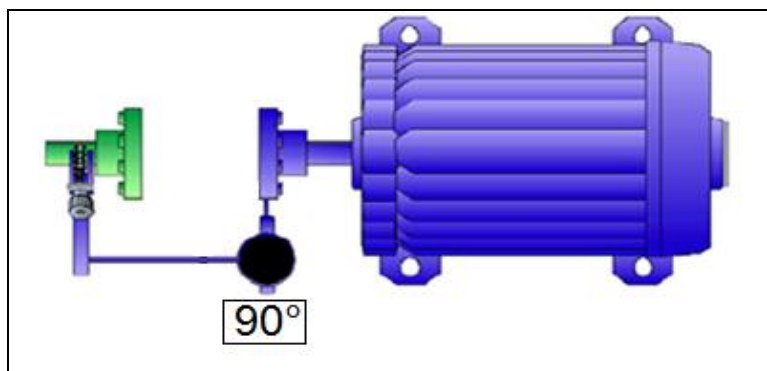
Posición 90° de medición RIM. Vista superior de motor.
